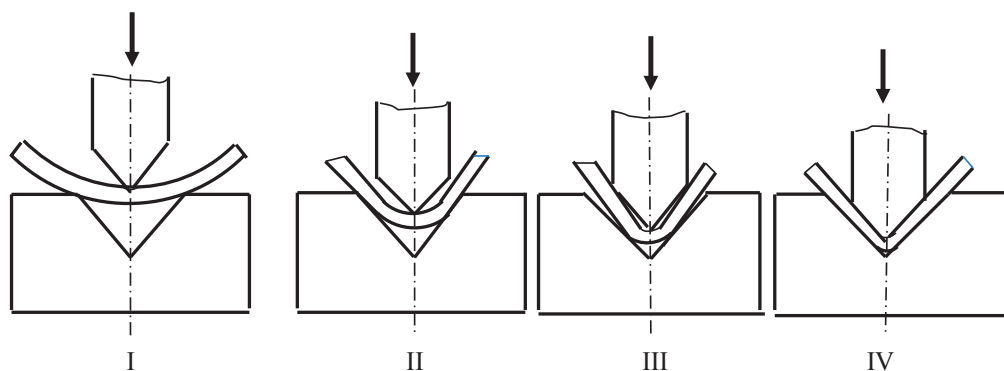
Стадии процесса одноугловой гибки в штампе
